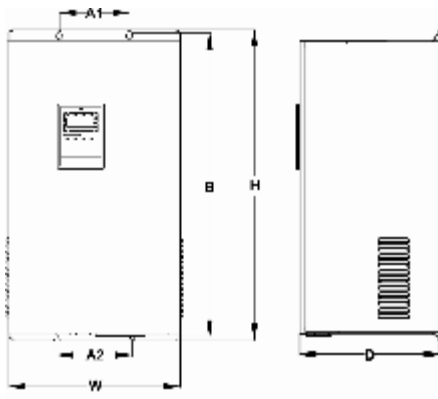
壁挂式能量回馈单元外形尺寸及安装尺寸
